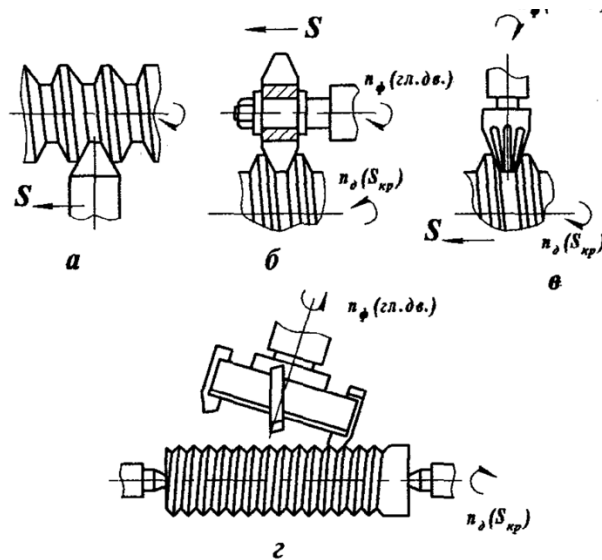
Основні методи нарізування різьби: а – різьбовий різець; б – однопіткова дискова фреза; в – однопіткова кінцева фреза; г – однопіткова торцева фреза
